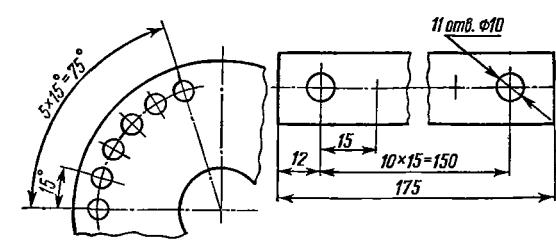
Нанесение размеров между равномерно расположенными одинаковыми элементами
